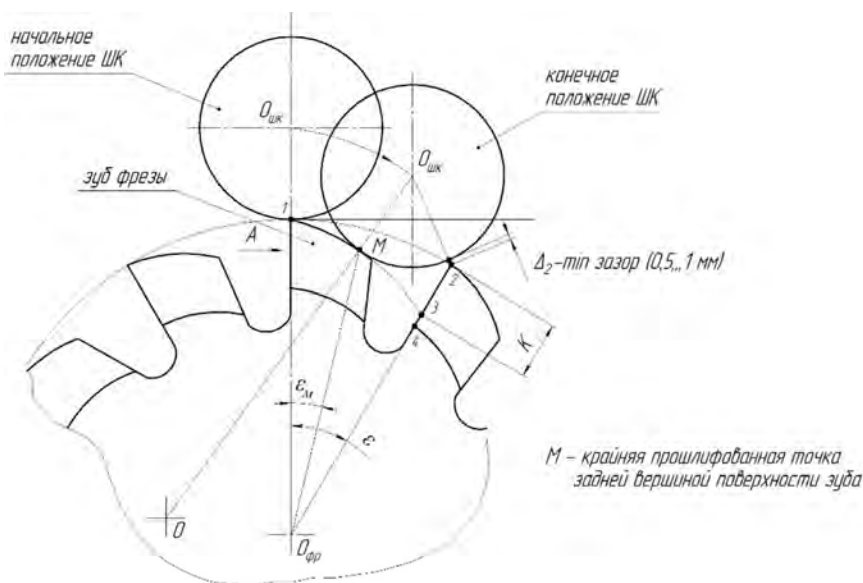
Схема затылования дисковой фрезы цилиндрическим шлифовальным кругом
